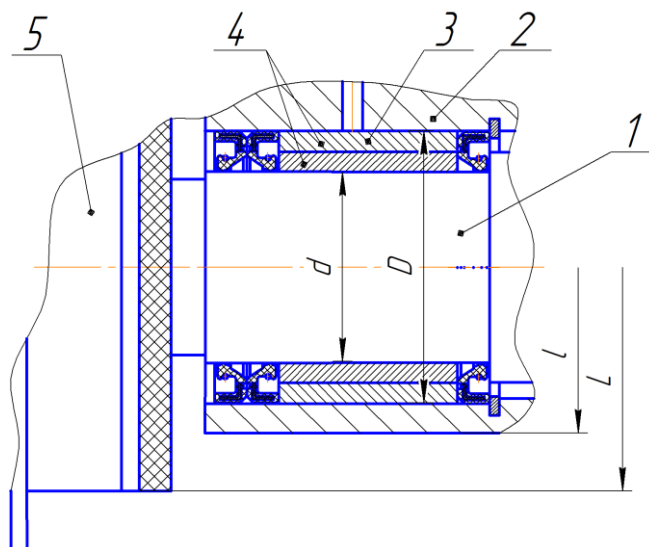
Будова підшипникової опори ножового вала кутера з гідродинамічним підшипником ковзання
